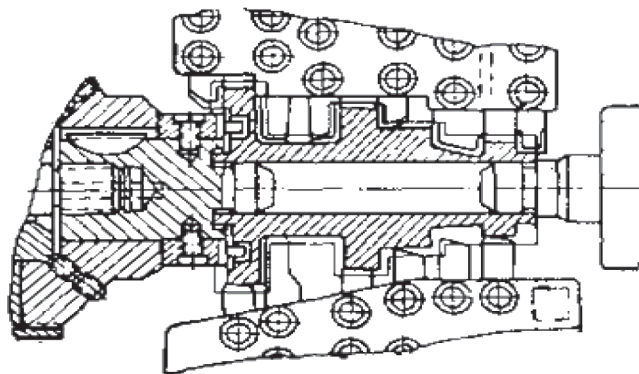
Суміщення в часі основних переходів при багаторізцевому обробленні блока зубчастих коліс
